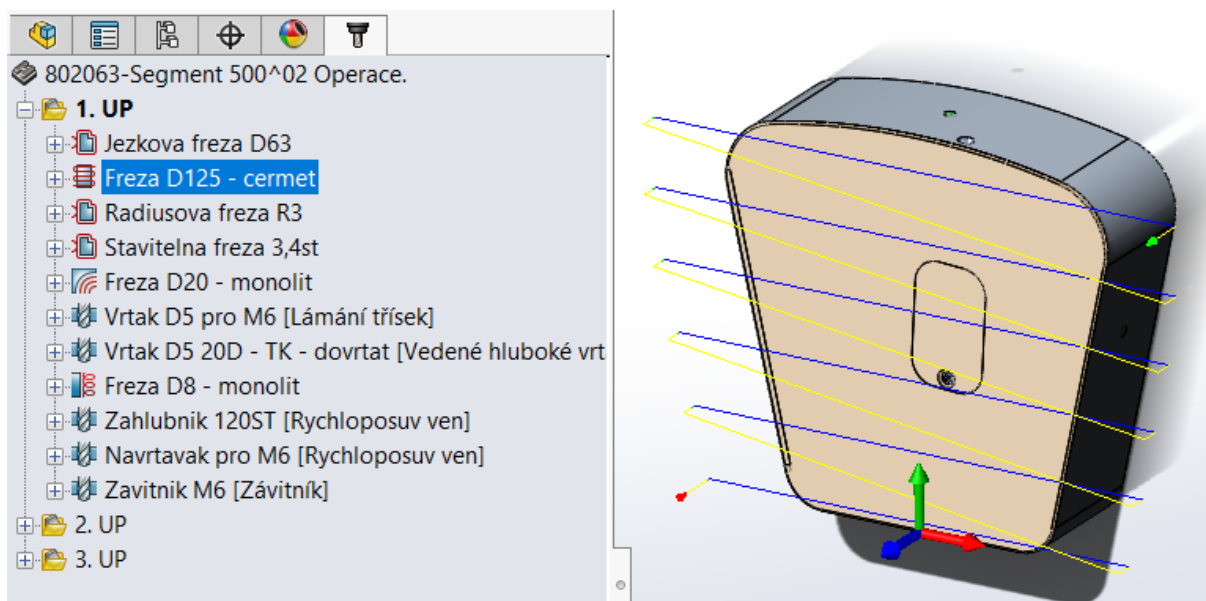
Nástroj operace Ježková fréza D63 [10]
